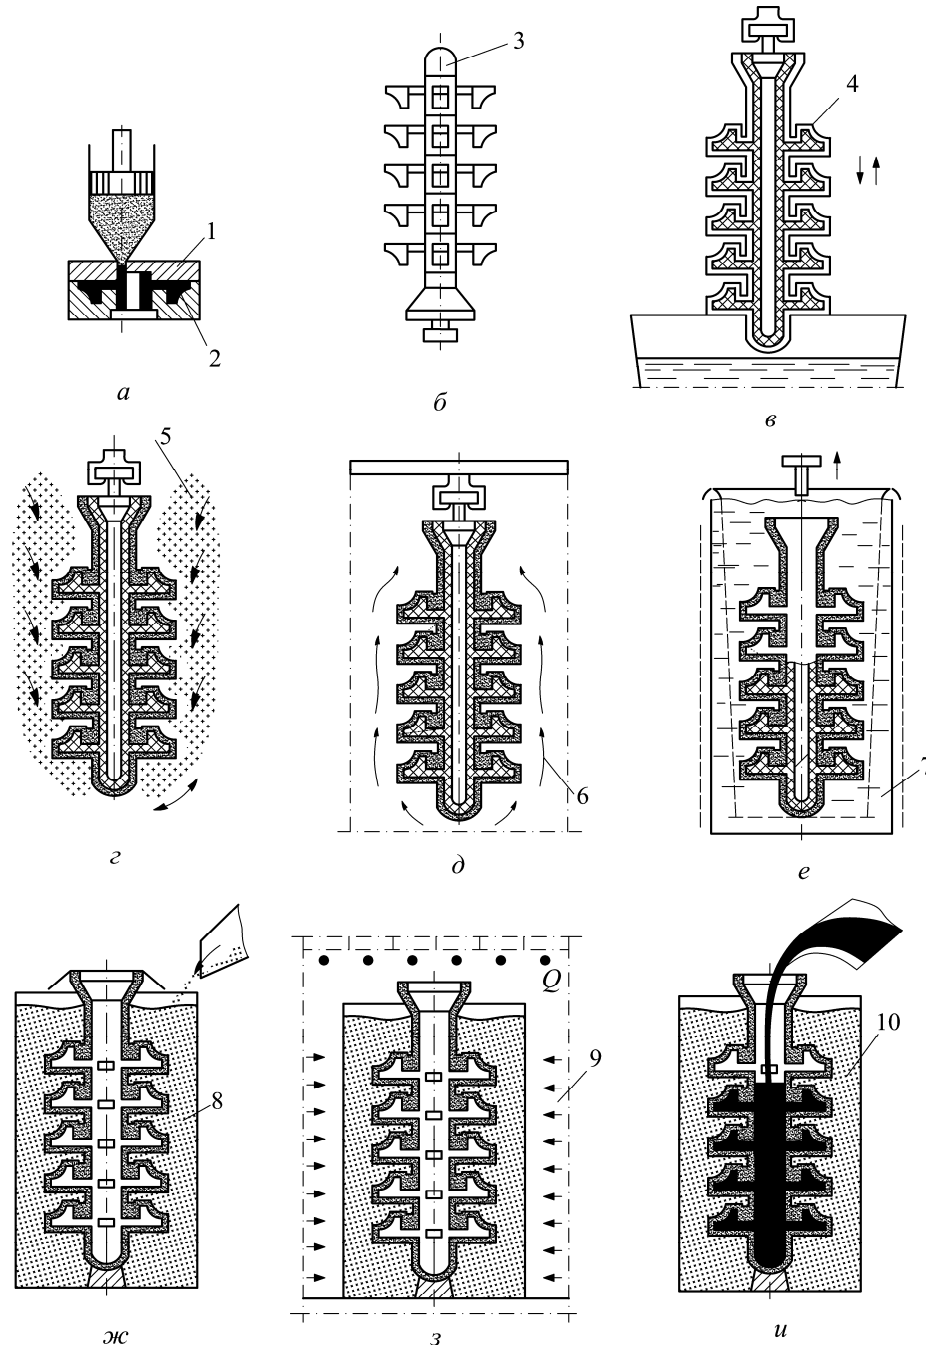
Последовательность изготовления многослойной оболочковой формы по выплавляемым моделям: *а* – запрессовка модельного состава в пресс-форму; *б* – сборка блока; *в* – нанесение на блок суспензии; *г* – обсыпка огнеупорным зернистым материалом; *д* – сушка; *е* – удаление модели; *ж* – засыпка опорным материалом; *з* – прокалка в печи; *и* – заливка формы расплавом; 1 – пресс-форма; 2 – модель; 3 – блок моделей отливок и литниковой системы; 4 – слой суспензии; 5 – огнеупорный зернистый материал; 6 – пары аммиака; 7 – горячая вода; 8 – опорный материал; 9 – печь; 10 – прокаленная форма; Q – подвод теплоты
